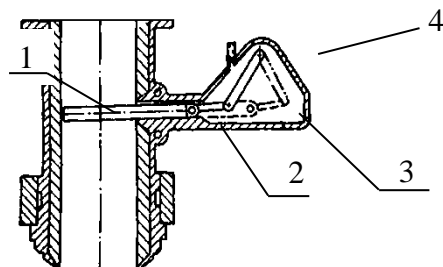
Шиберное устройство для регулирования расхода дутья через фурму печи: 1 – неподвижный патрубок; 2 – шибер; 3 – рычаг; 4 – кожух
